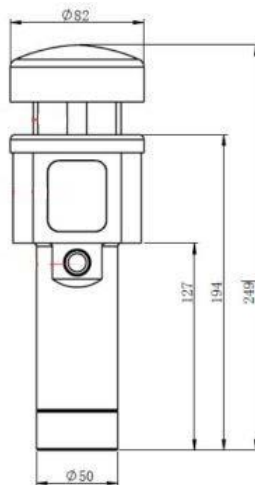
а. Внешний вид и габаритные размеры изделия
